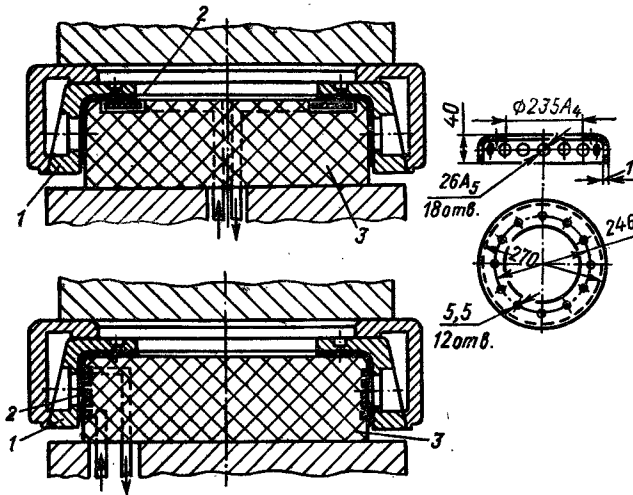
Примеры освоённых операций штамповки и индукторы к ним: вырезка центрального окна и пробивка 30 отверстий (за две операции с разными индукторами): 1 — матрица (кольцо); 2 — медный индуктор (плоский индуктор однорядковый); 3 — баллиновый корпус
